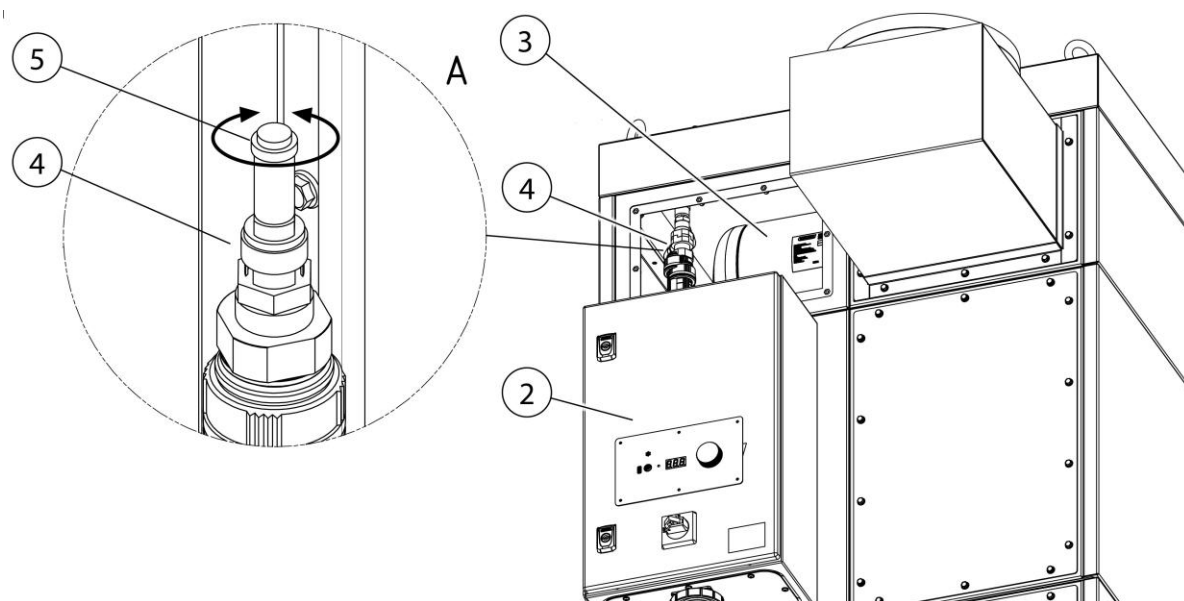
Проверка предохранительного клапана сжатого воздуха
